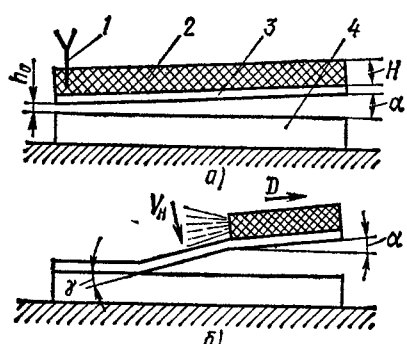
Принципиальная схема сварки взрывом:
